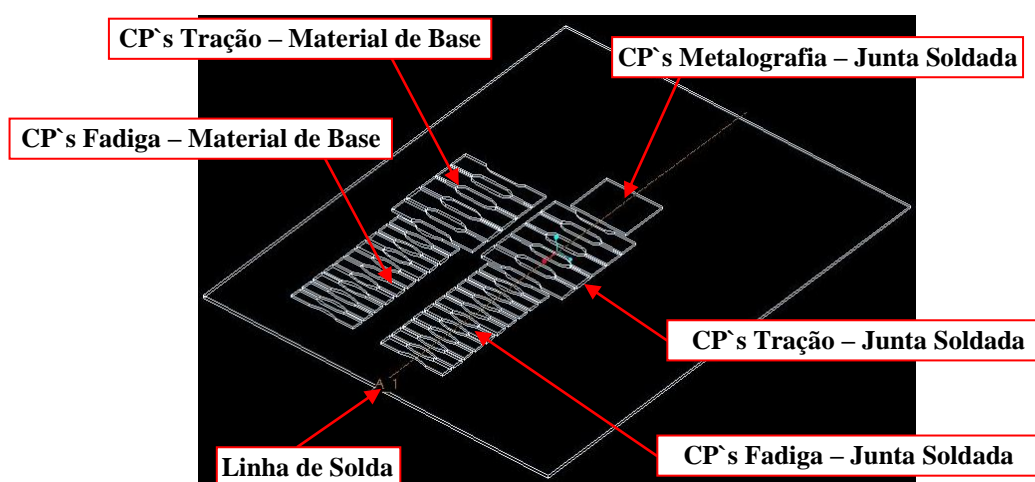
Ilustração de retirada dos corpos de prova das chapas soldadas.
